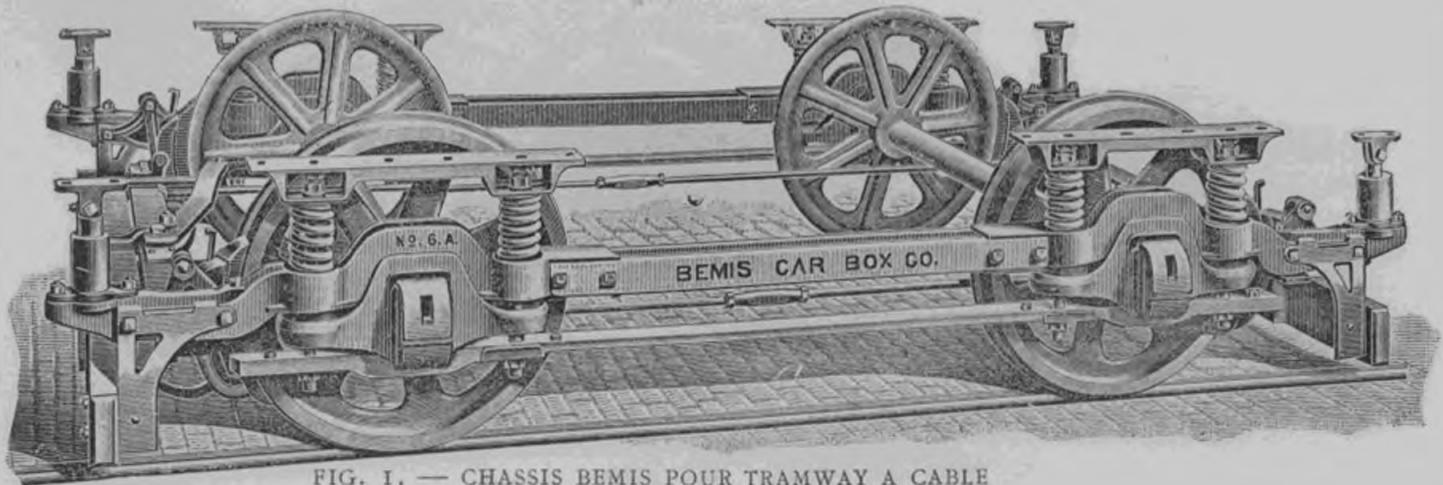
CHASSIS BEMIS POUR TRAMWAY A CABLE
